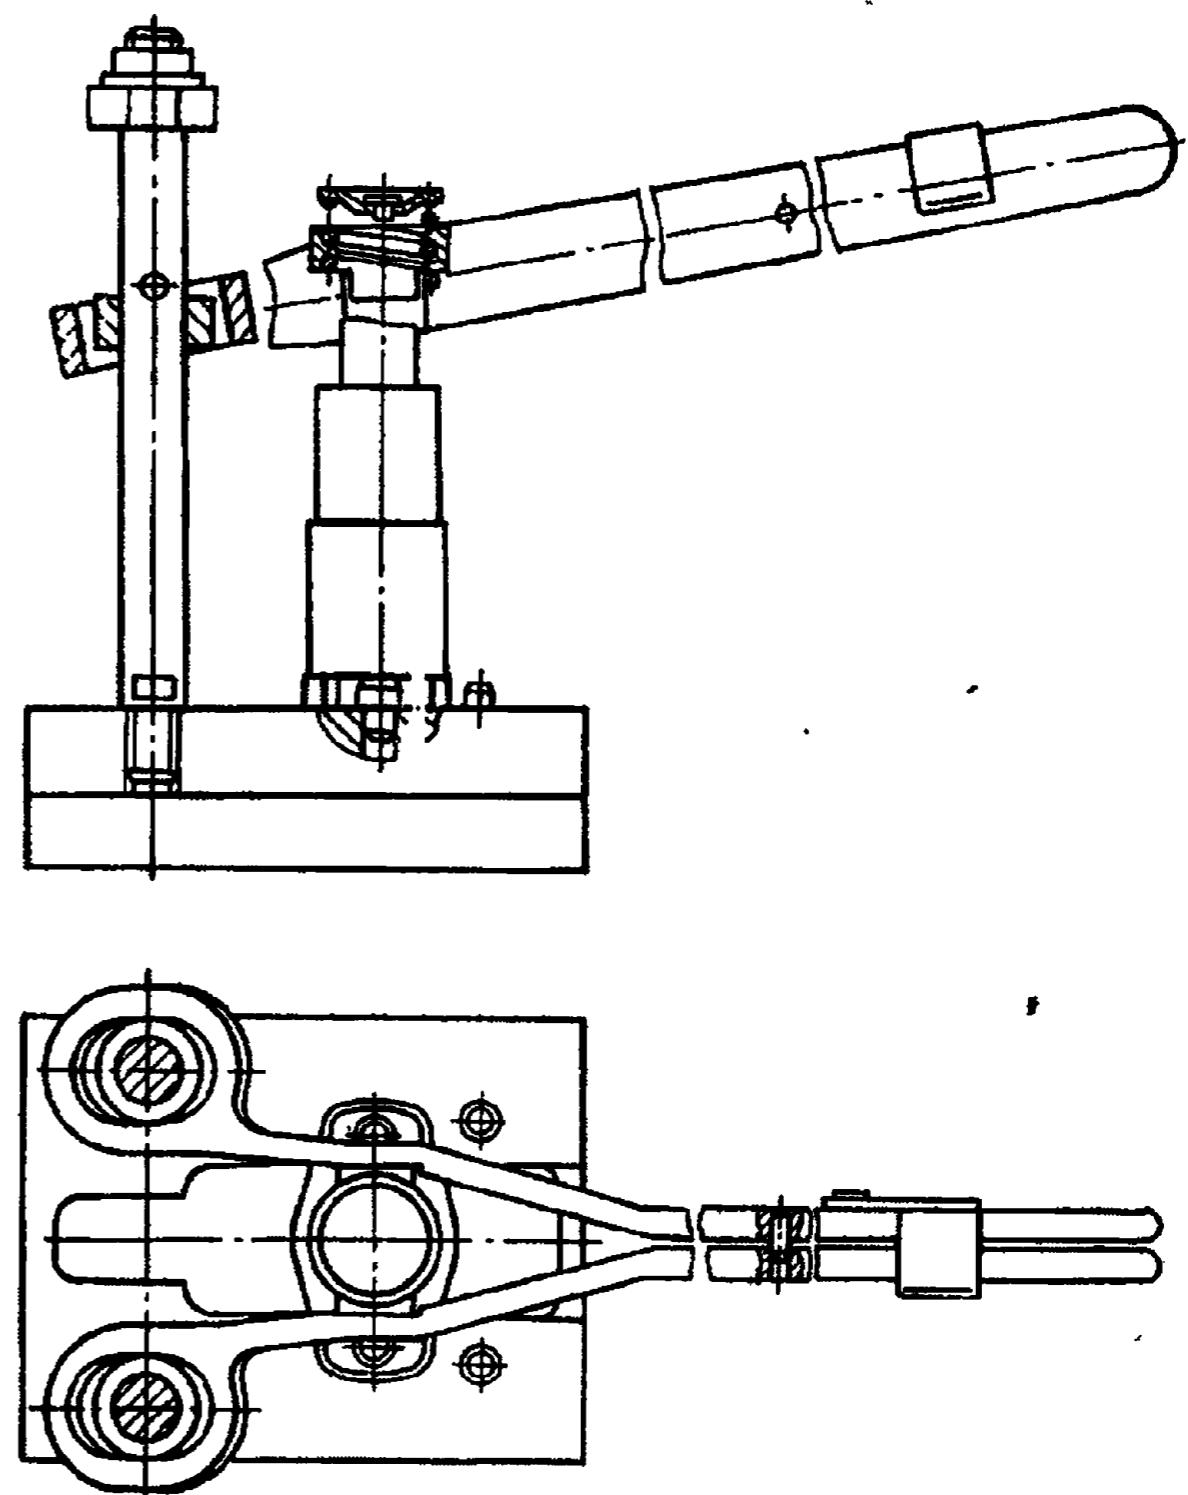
Установка насосной секции ТНВД в приспособление И801.20.000 для разборки-сборки
